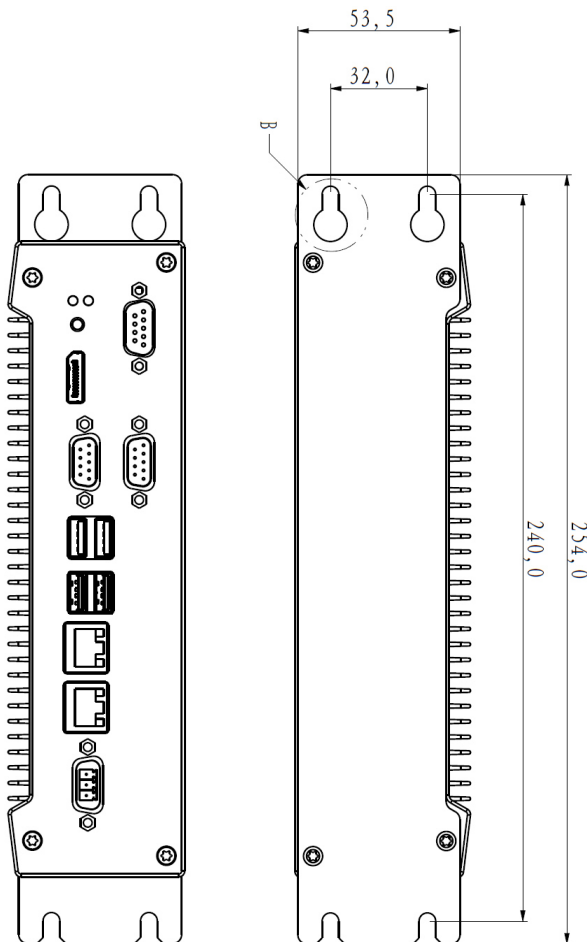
KBox A-101 mit montierter Halterung für Gehäusemontage
